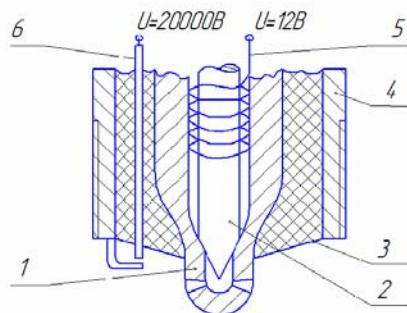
Схема реалізації свічки запалювання та форсунки подачі палива в одному корпусі
